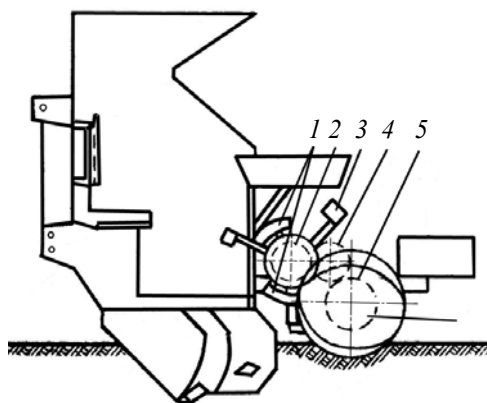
Схема привода посадочного аппарата с зубчатой передачей:
